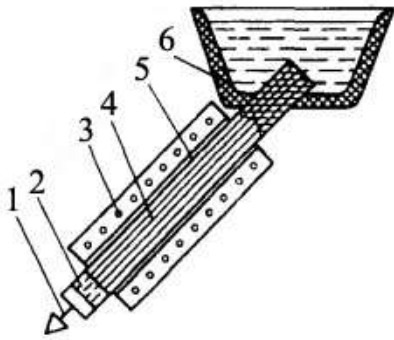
Схема вакуумного просочення армуючого каркасу КМ: 1 – підвід до вакуумного насоса; 2 – пориста пробка; 3 – піч опору; 4 – волокна; 5 – форма; 6 – тигель з розплавленим матеріалом матриці
